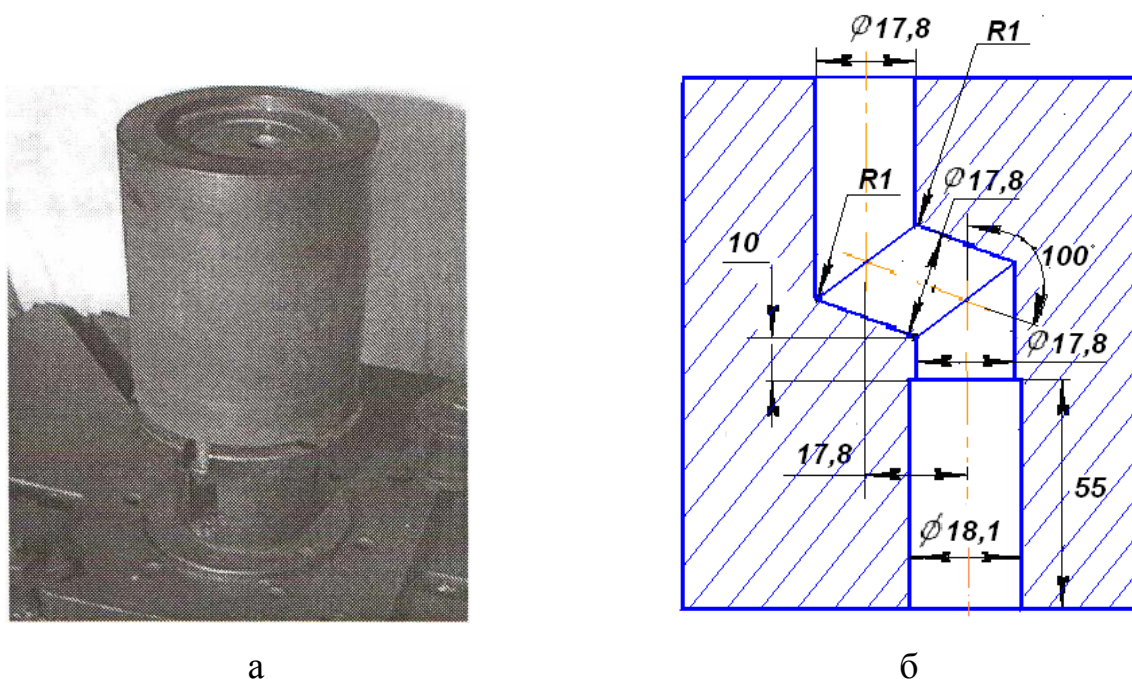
Инструмент для РКУП в ПК цилиндрической заготовки:
